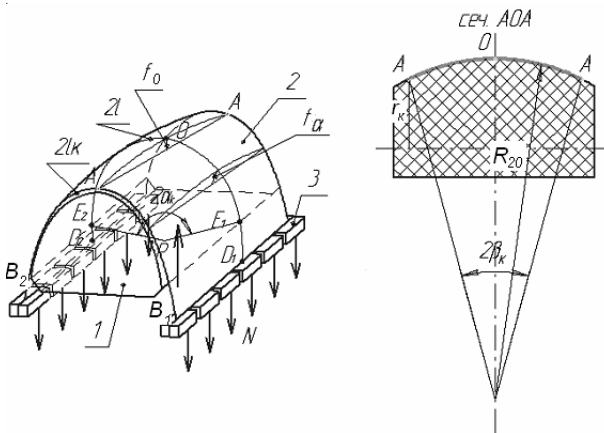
Схема обтяжки по обтяжному пуансону 1 заготовки 2, удерживаемой в зажимах пресса 3
